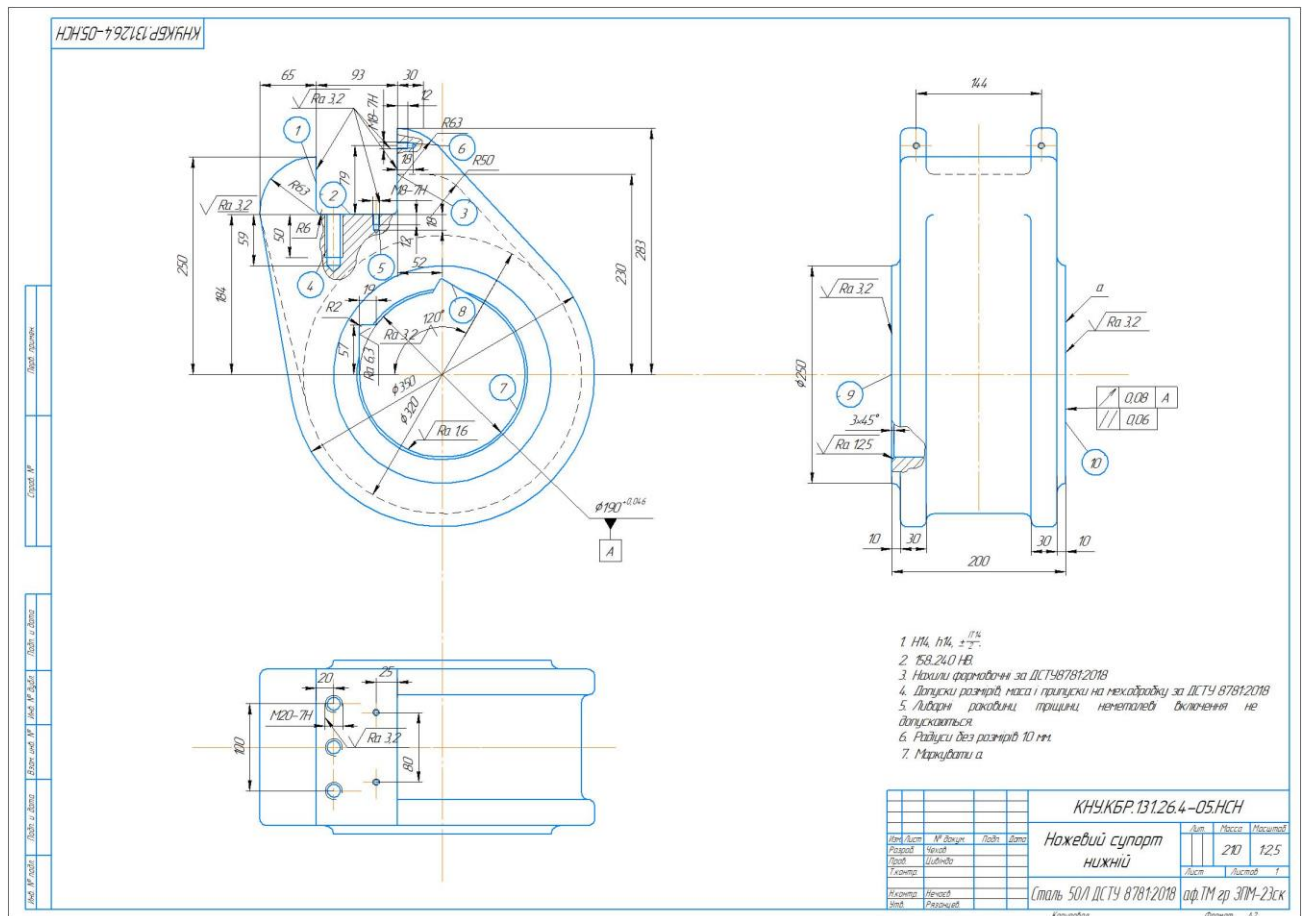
Пронумеровані поверхні ножового супорту нижнього
